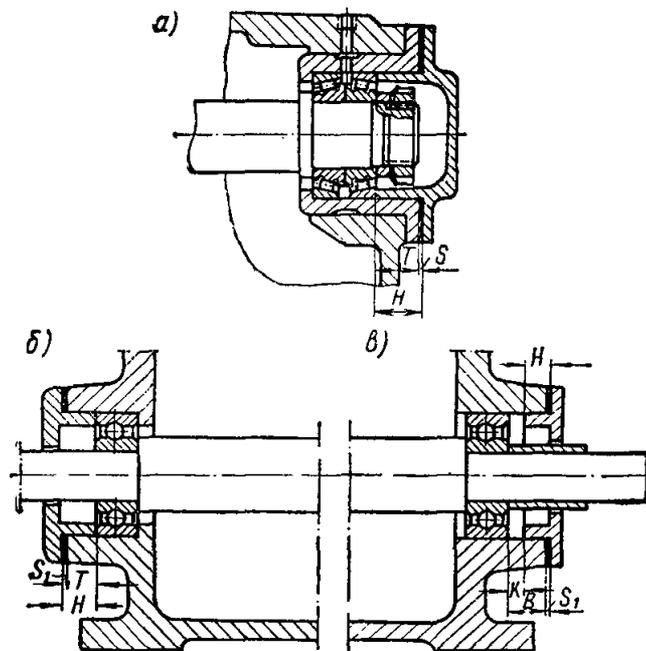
Контроль за установкой крышек в узлах с подшипниками
